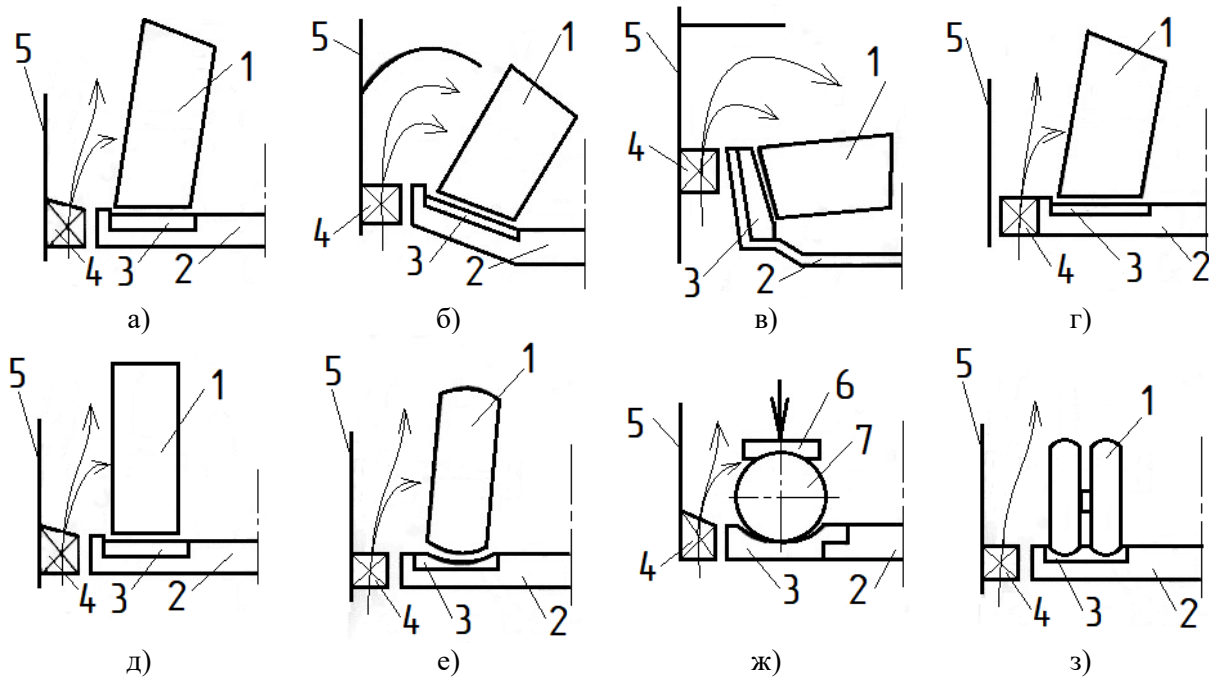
Основні схеми розташування робочих елементів у вертикальних валкових млинах: 1 – валок; 2 – помольний стіл; 3 – бронеплита; 4 – пристрій подачі повітря; 5 – корпус млина; 6 – напірне кільце; 7 – кулі.
